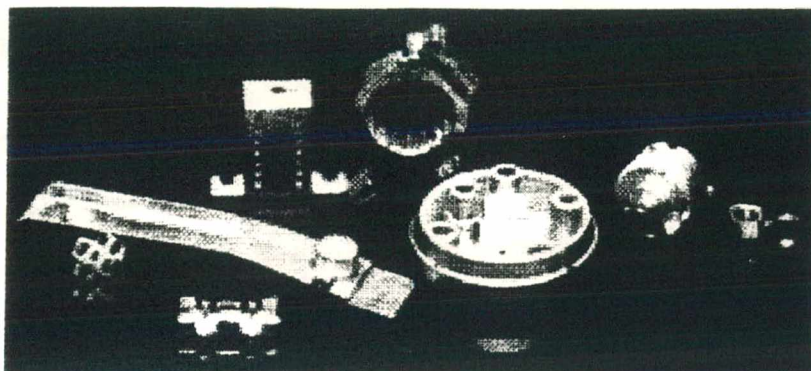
Peças complexas obtidas por moldagem por injeção de pós
